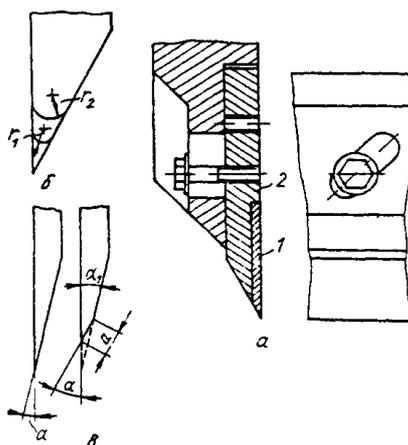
Устройство ножа: 1 – лезвие ножа; 2 – корпус ножа
